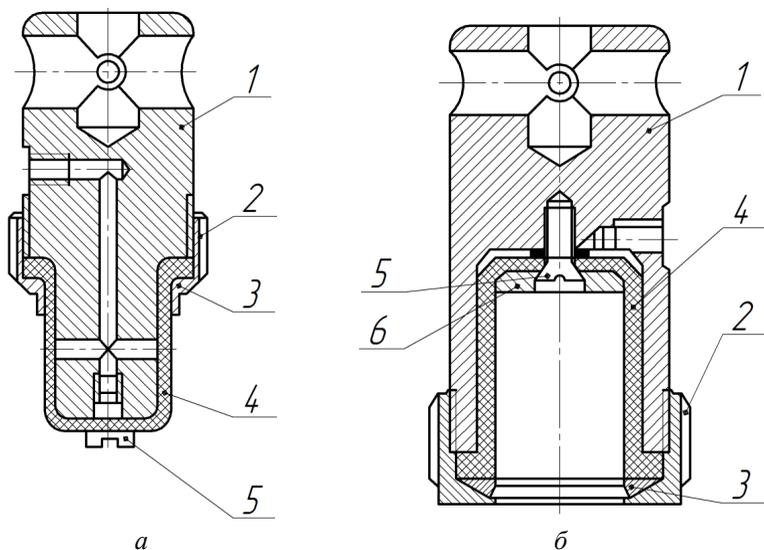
Центрирующие ЗУ с расширяющимися эластичными камерами фирмы *Simrit* (Германия) для взятия объектов за поверхность: *а* – внутреннюю; *б* – наружную; 1 – корпус; 2 – гайка; 3 – кольцо; 4 – камера; 5 – винт; 6 – шайба
